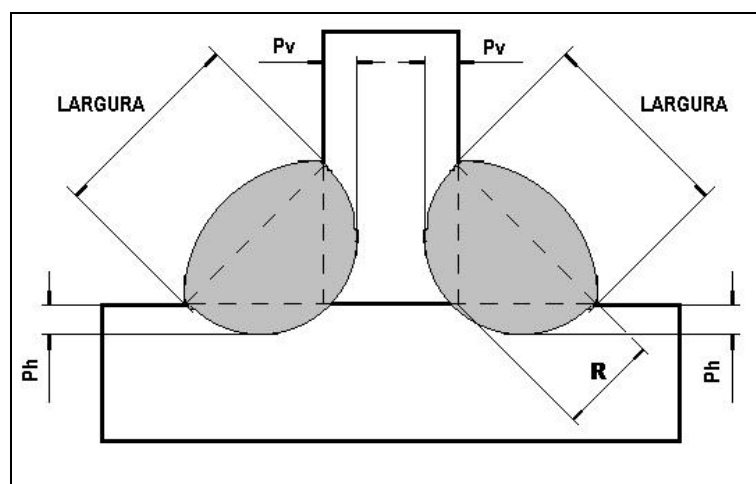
Seção transversal de uma junta soldada em “T” e geometria do cordão de solda
